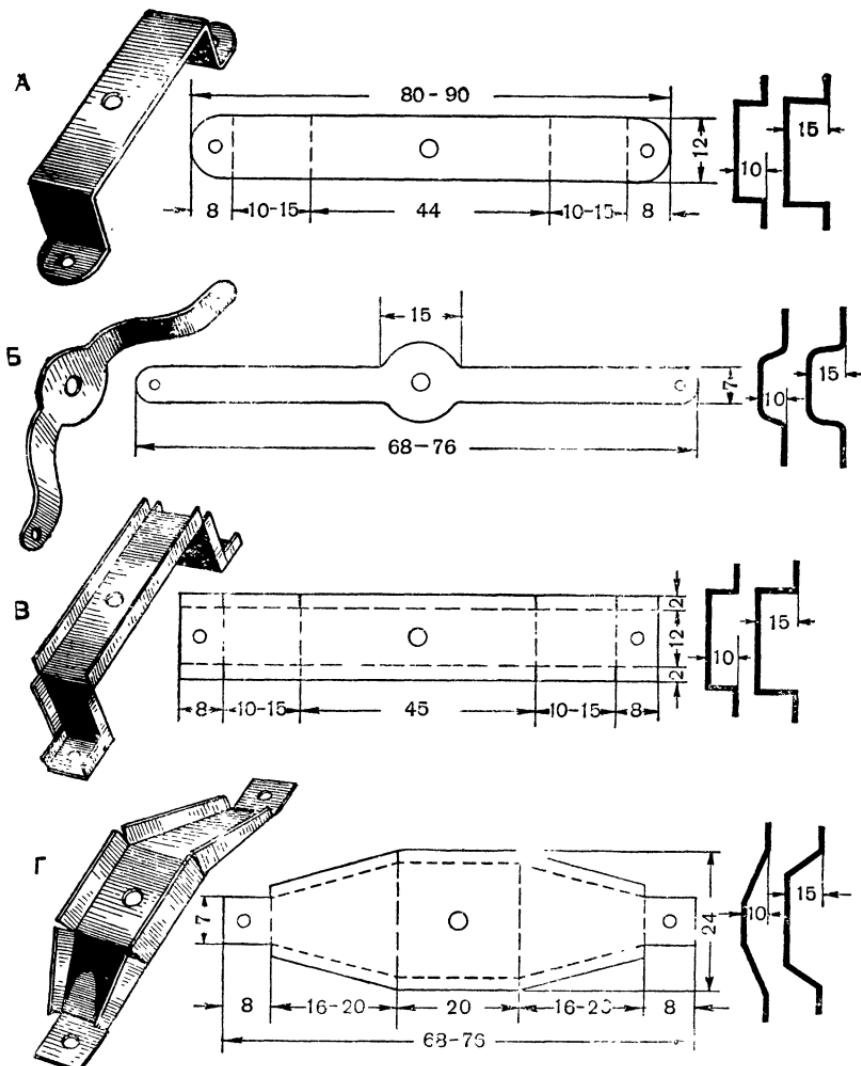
Подшипниковые щиты с двумя лапками. Слева—общий вид; в середине—заготовка; справа—профили заднего и переднего щитов.
